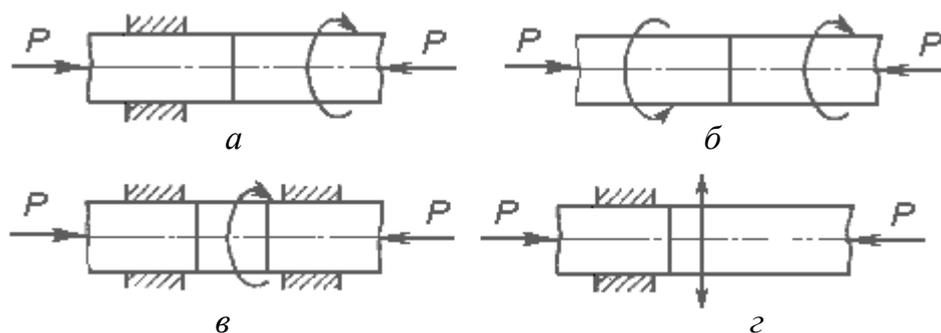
Принципиальные схемы сварки трением
